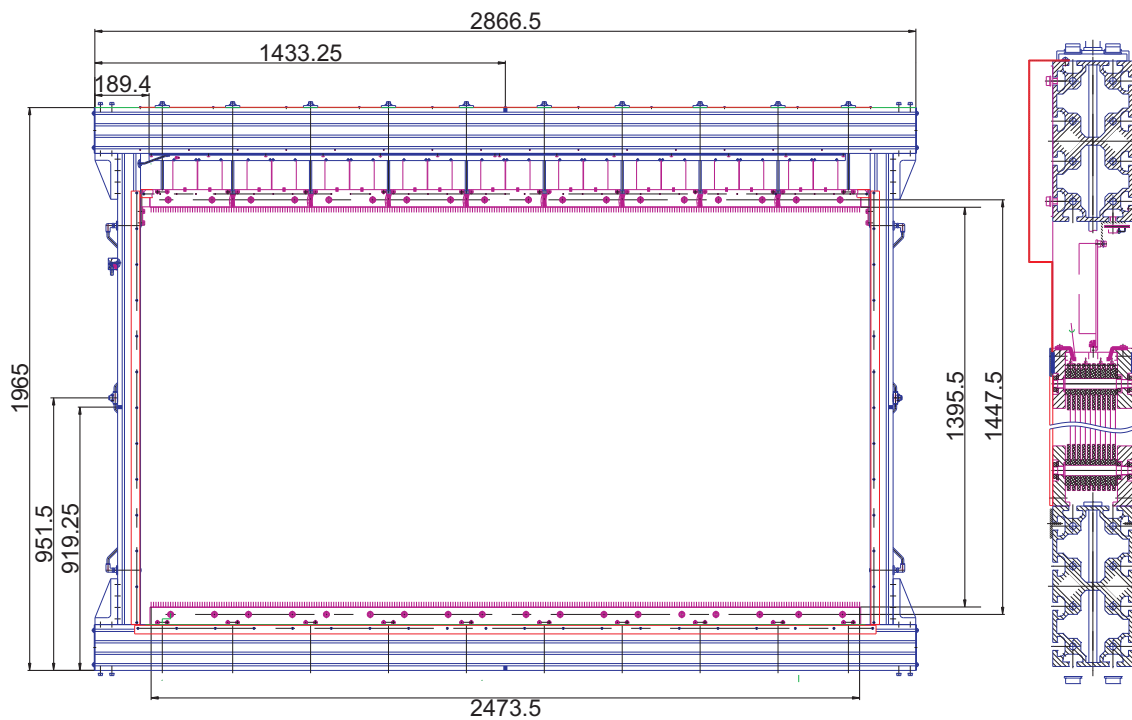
Technische Zeichnung der X-Driftkammer [ $M^+$ ]
